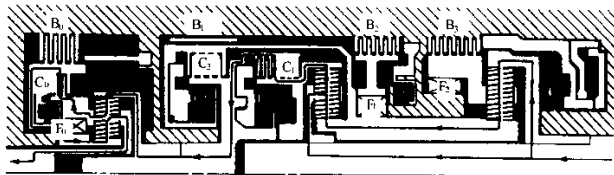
1 档齿轮 (换档杆置 L 位置)、发动机制动结构简图
